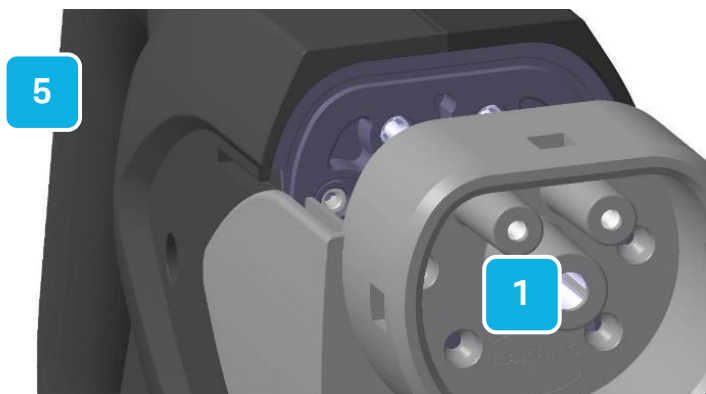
Steckergesicht Ladestecker Harting CCS2, auf Ladestecker aufschieben
